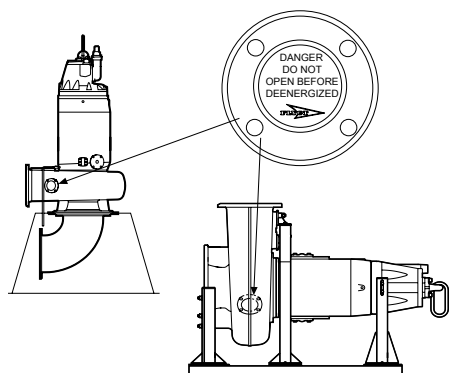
Установка типа T (слева) и установка типа Z. (Показан стандартный насос.)
